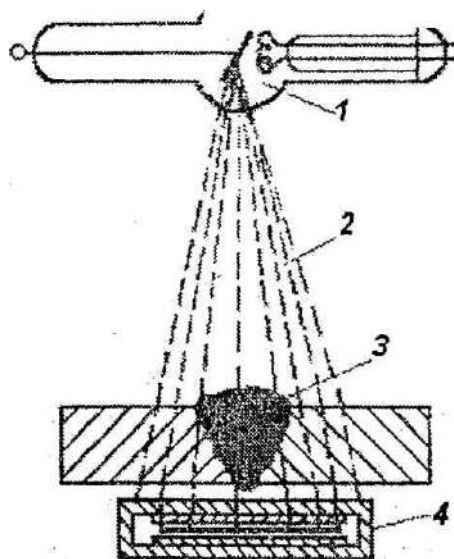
Рентгеновское просвечивание сварного шва:
